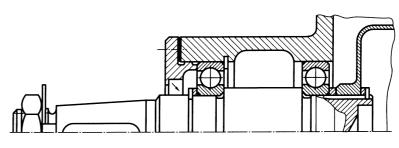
Выходной вал волнового зубчатого редуктора
